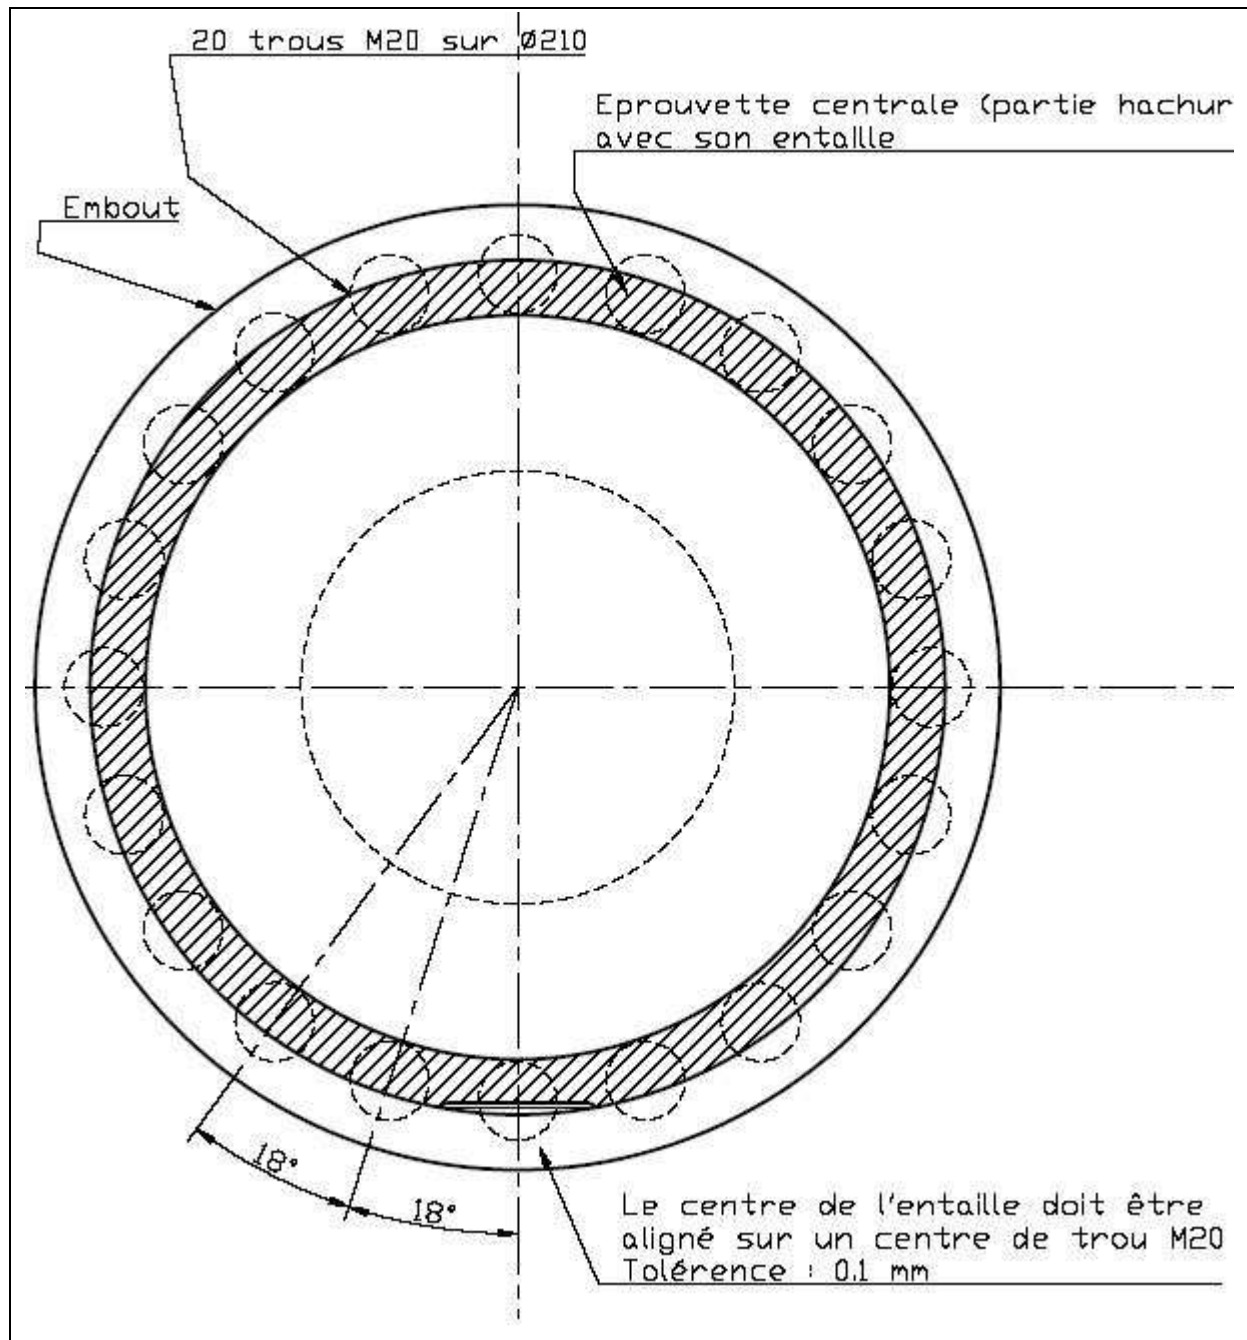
Plan de montage de l'éprouvette pour la préfissuration – Vue axiale.
